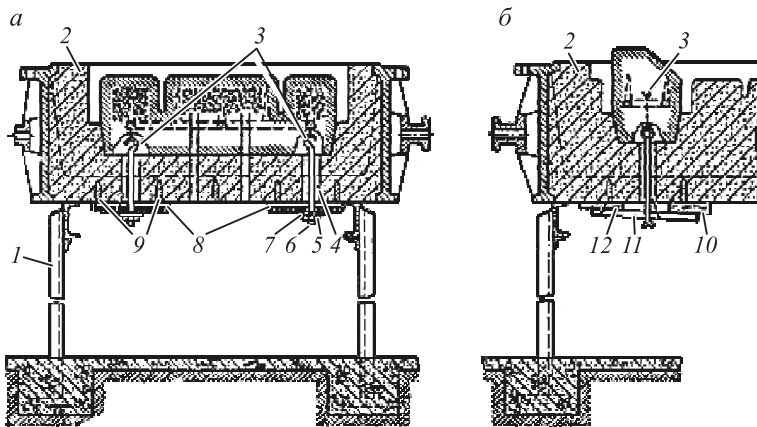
Технологические операции крепления стержней к верхней полуформе: а – крючками; б – проволокой; 1 – стэнд; 2 – полуформа; 3 – подъемы стержней; 4 – отверстия в полуформе; 5 – гайки; 6 – крючки; 7 – шайбы; 8 – планки; 9 – крестовины опоки; 10 – клин; 11 – брусок; 12 – планка
